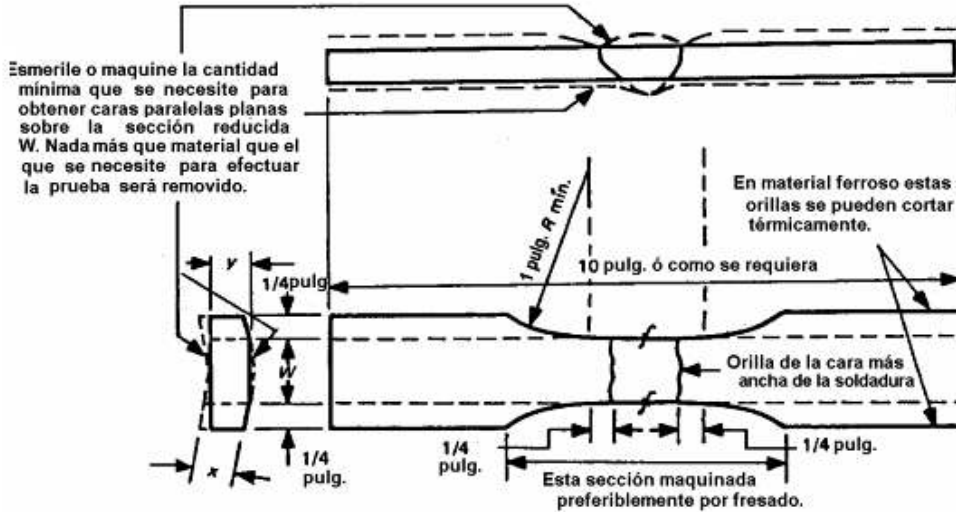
Dimensiones de probeta para ensayo de tracción.
